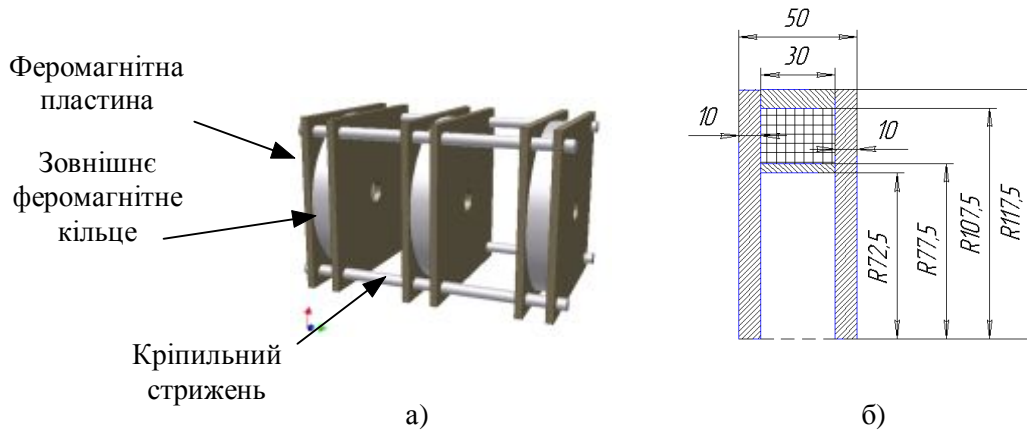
Дискова конструкція ІР з феромагнітними пластинами
